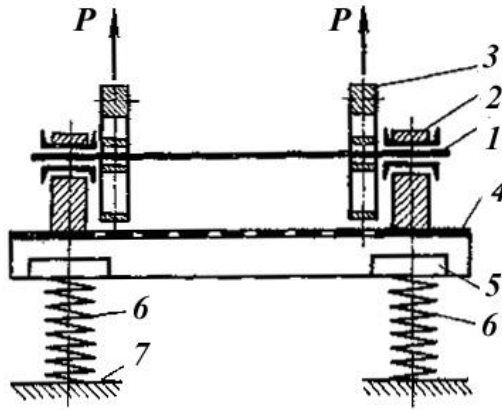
Вібраційний грохот: 1 – вал; 2 – підшипник; 3 – дебаланс; 4 – короб із ситами; 5 – рама короба; 6 – опорні пружини; 7 – станина
